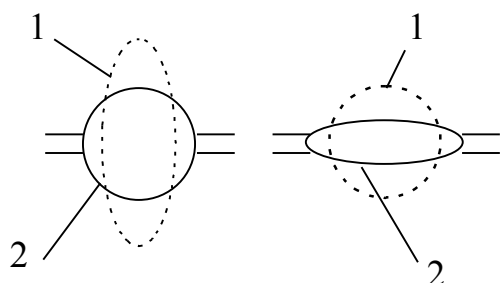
Схема системы калибров овал-круг: 1 - контур заготовки; 2 - контур калибра.
